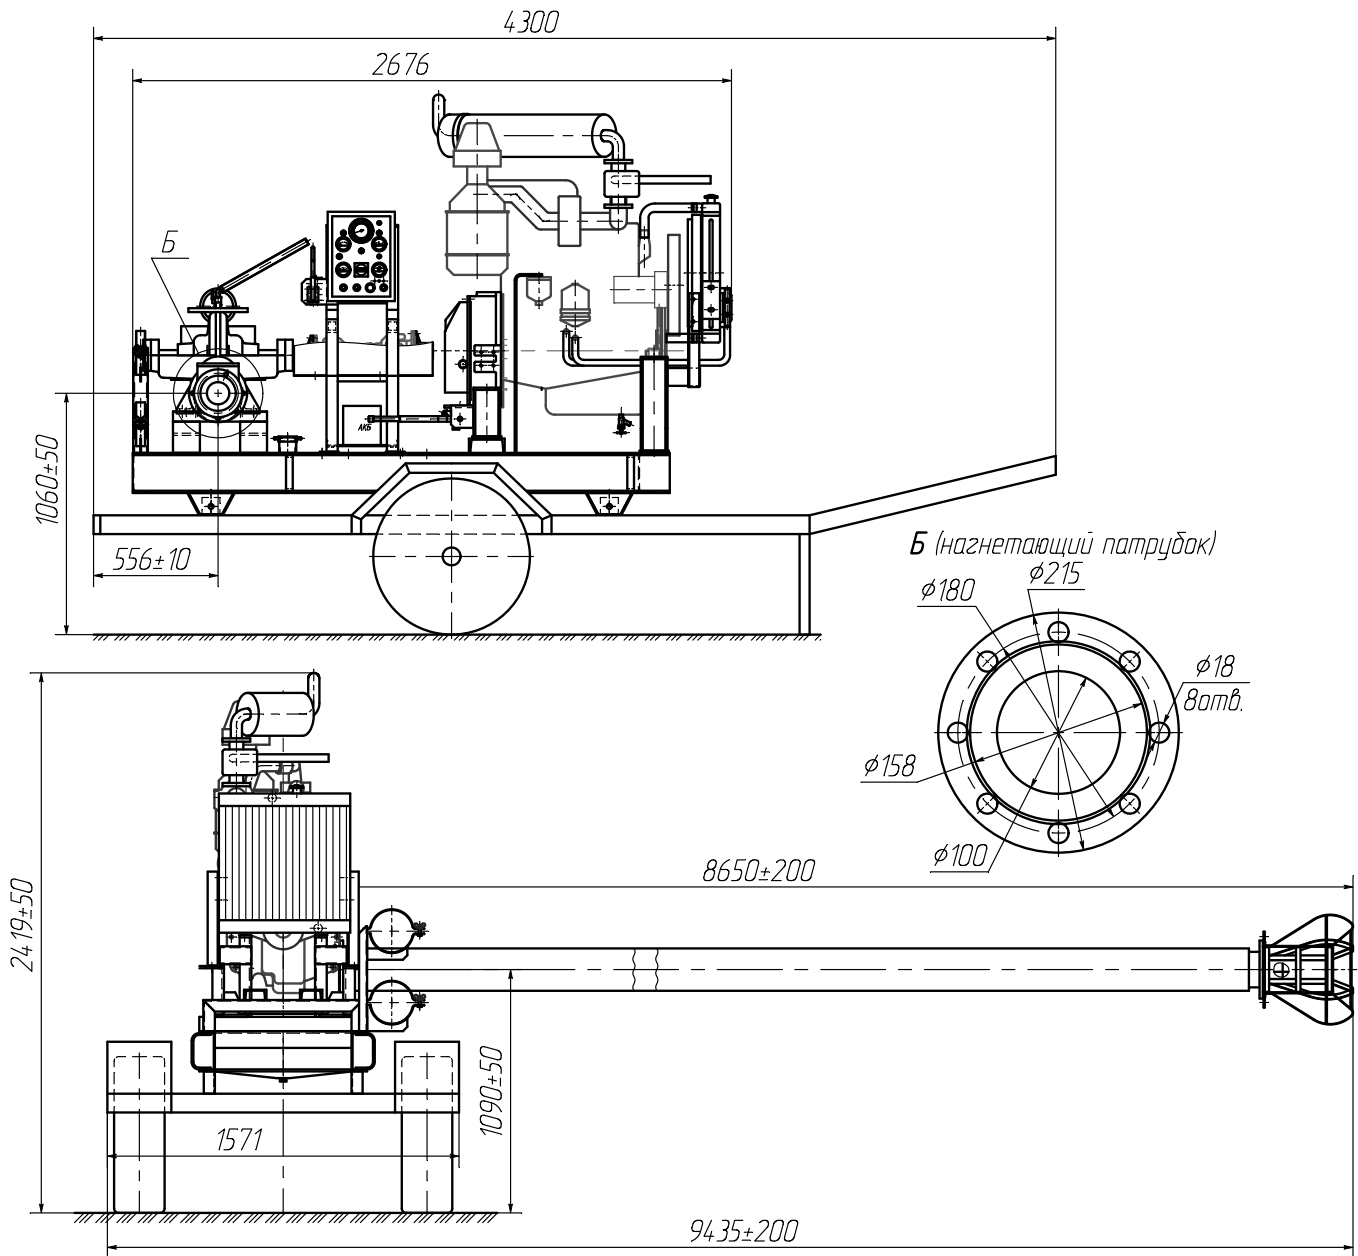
Общий вид агрегатов типа ДНА-П
